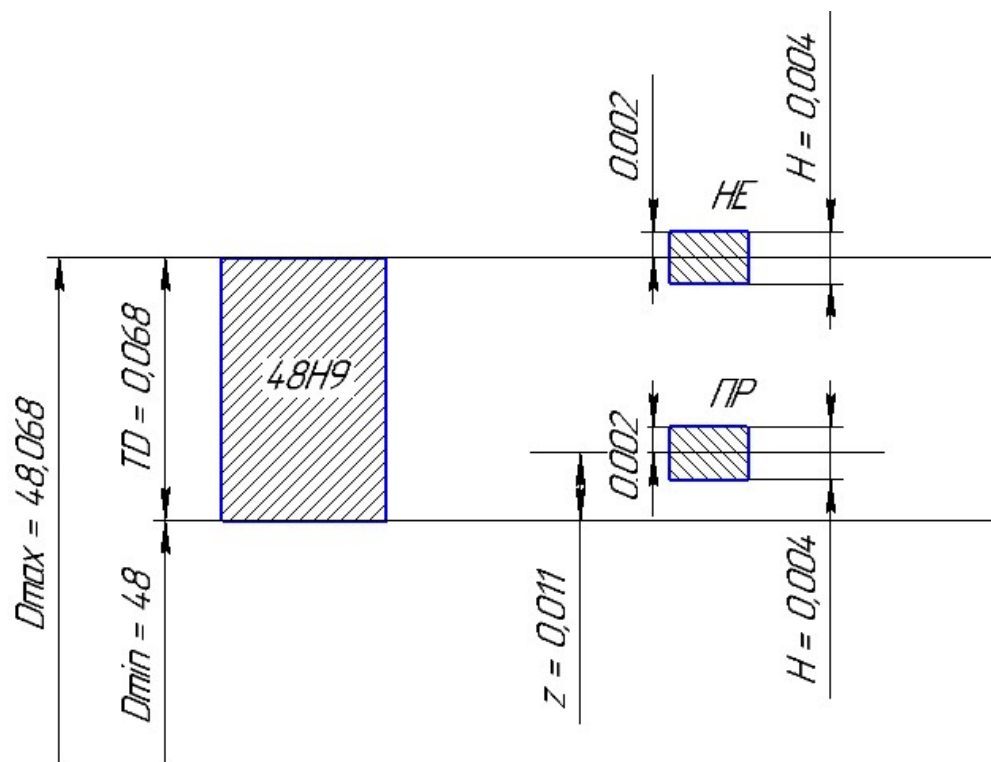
Схема розташування поля допусків калібр – пробки
